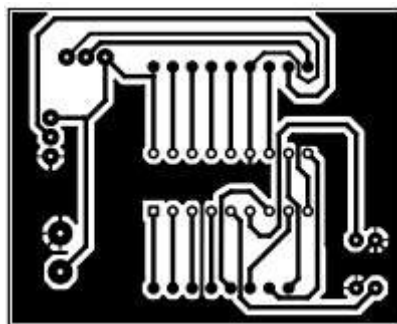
Diseño de las pistas del motor Unipolar para la placa PCB.
